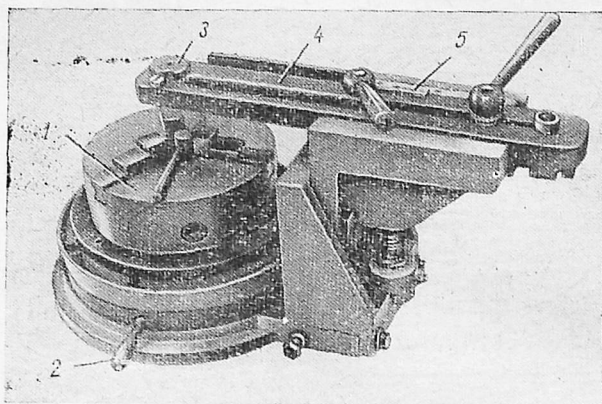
Приспособление для сверловки отверстий во фланцах.
